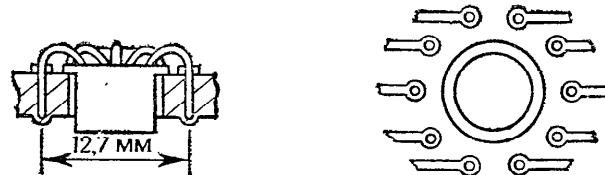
Два способа установки корпуса ТО-5 на плату.
